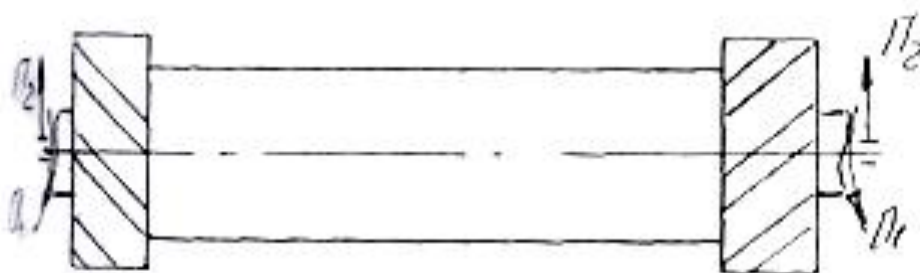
Схема обробки торцевими фрезами з нерухомою заготовкою
